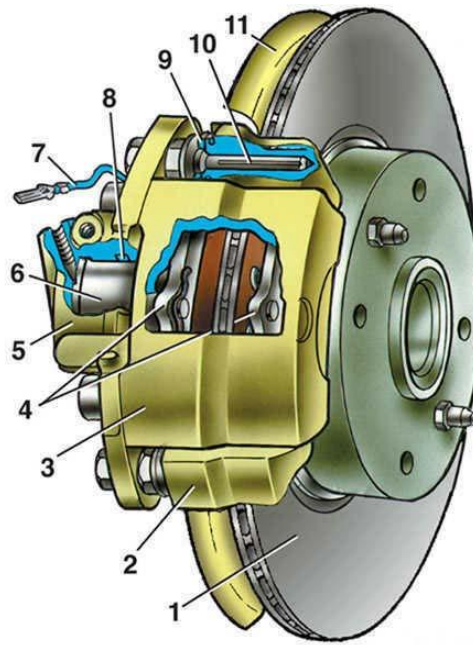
Гальмівний механізм переднього колеса автомобіля ВАЗ 2110: 1 – гальмівний диск; 2 – направляюча колодок; 3 – супорт; 4 – гальмівні колодки; 5 – циліндр; 6 – поршень; 7 – сигналізатор зношування колодок; 8 – ущільнювальне кільце; 9 – захисний чохол направляючого пальця; 10 – направляючий палець; 11 – захисний кожух
